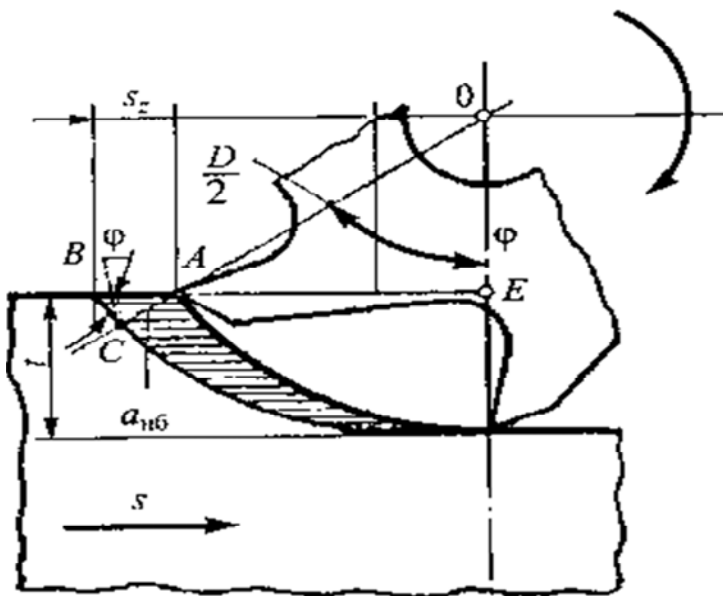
Схема изменения толщины стружки при фрезеровании
